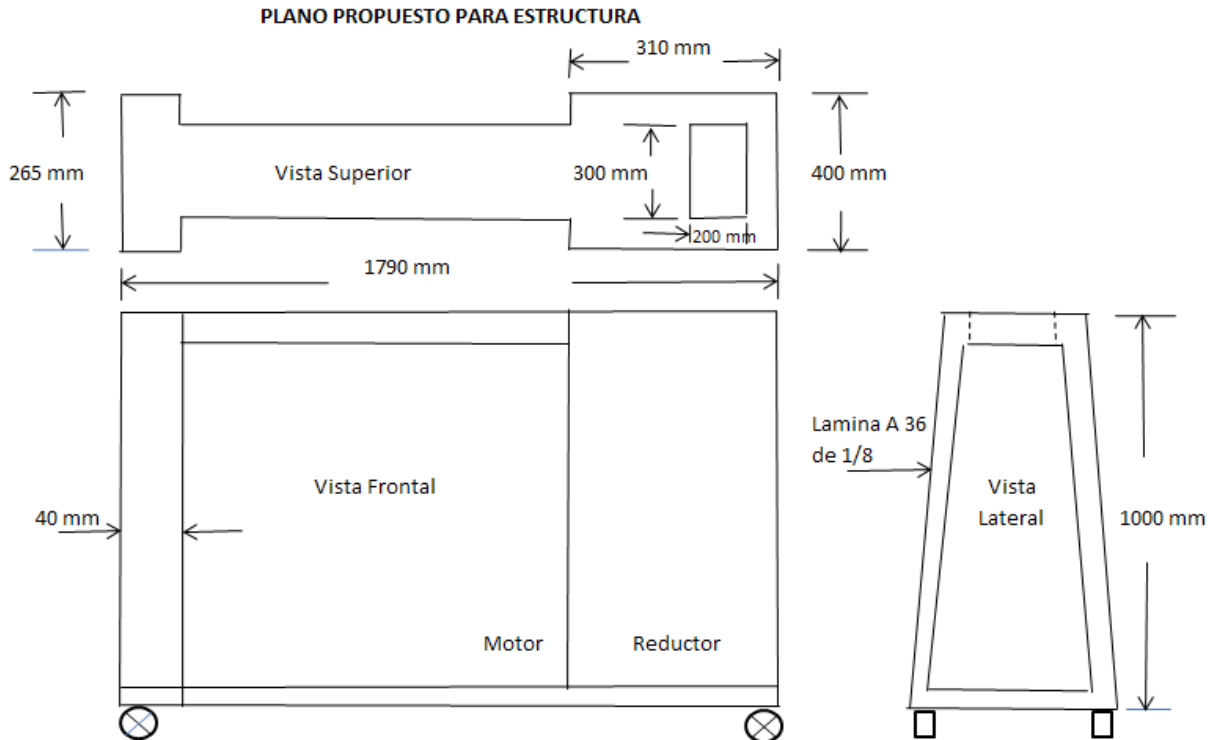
Plano propuesto para la estructura de la maquina extrusora.
